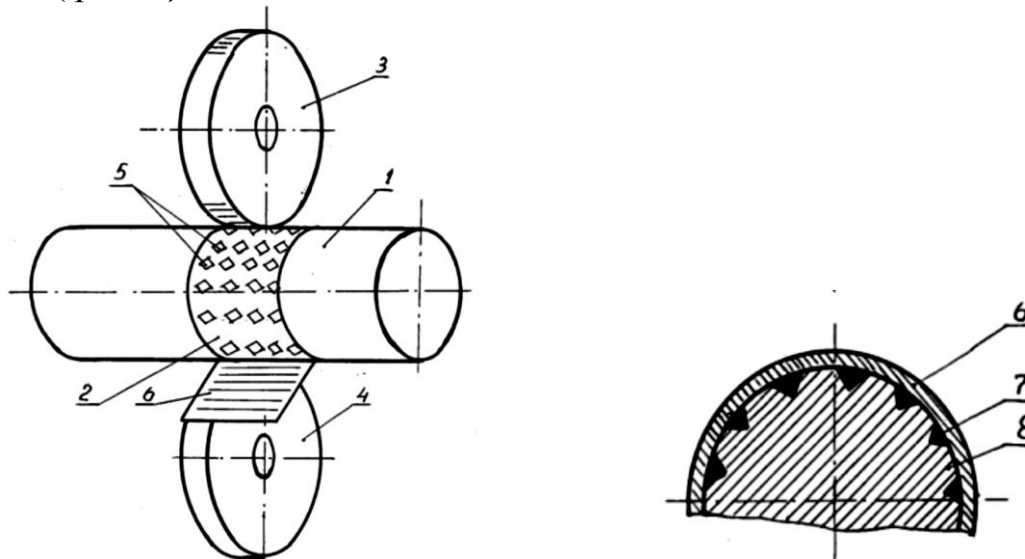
Базова схема відновлення зношених поверхонь: 1 – деталь; 2 – зношена поверхня; 3 і 4 – зварювальні ролики; 5 – осередки насічки; 6 – стрічка; 7 – западини з припоєм; 8 – гребені
